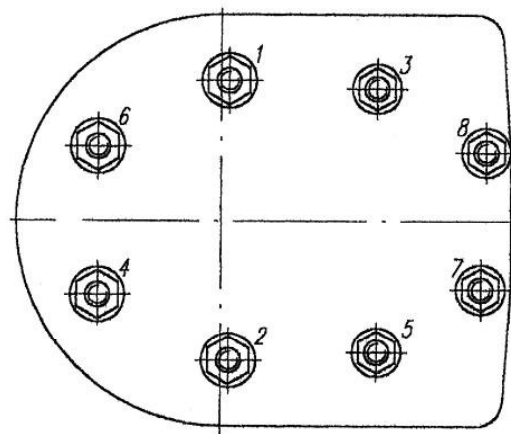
Схема затяжки шпилек крепления головки цилиндра
